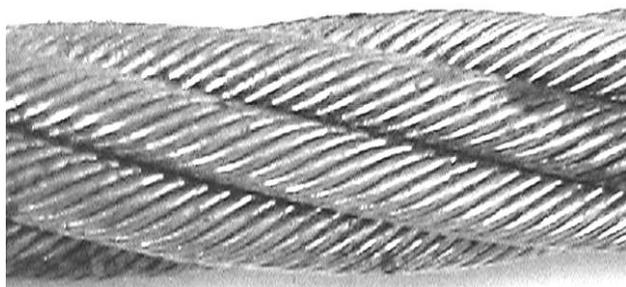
Образец № 3 каната двойной свивки диаметром 4 мм изготовленный с неравномерным натяжением прядей
